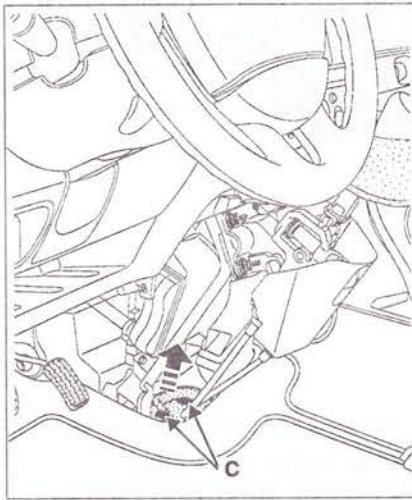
Приподнимите защитный материал, чтобы отвернуть две гайки C крепления направляющей тросов выбора и переключения передач.
